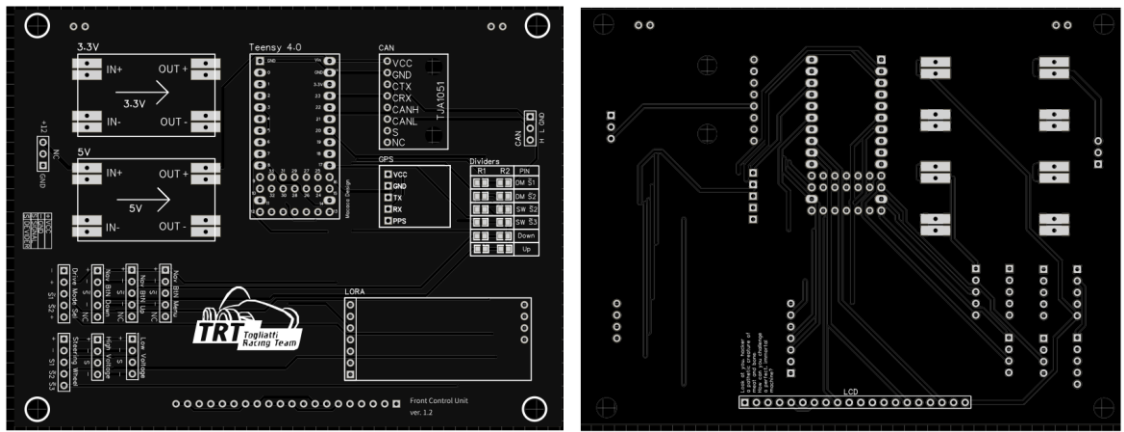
Двухмерный общий вид готовой платы с двух сторон
